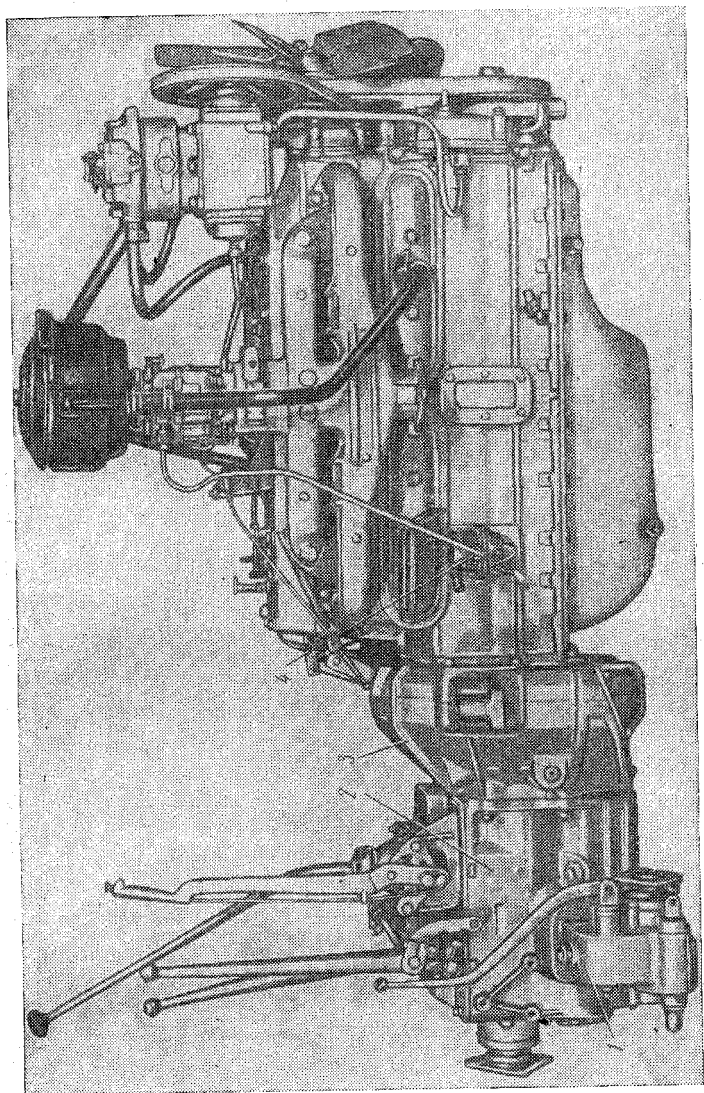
Двигатель со сцеплением, коробкой передач и коробкой отбора мощности (вид справа):
